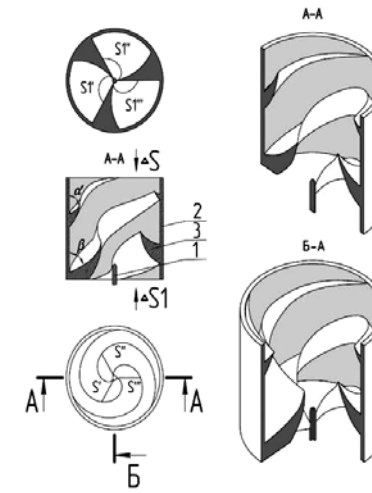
Турбіна з будовою лопатей за принципом золоті спіралі (1 – вал, 2 – порожнистий циліндричний корпус, 3 – спіралеподібна лопать)
